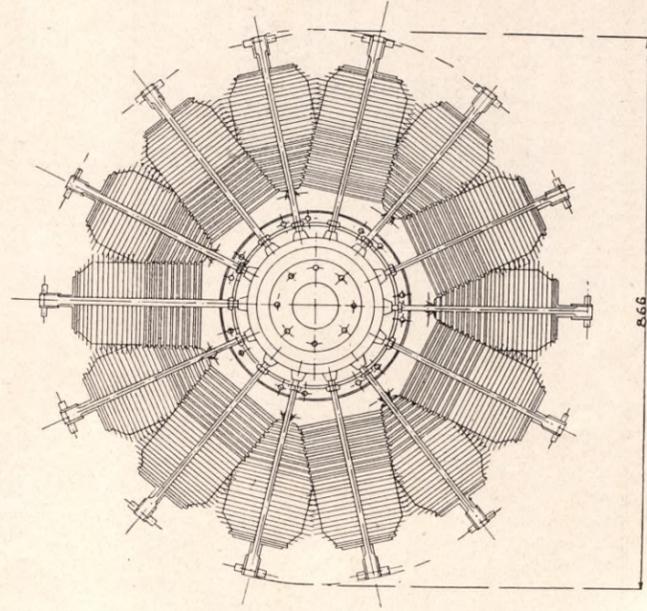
120 P 14-Zylindermotor, Raumzeichnung, Stirnansicht.
